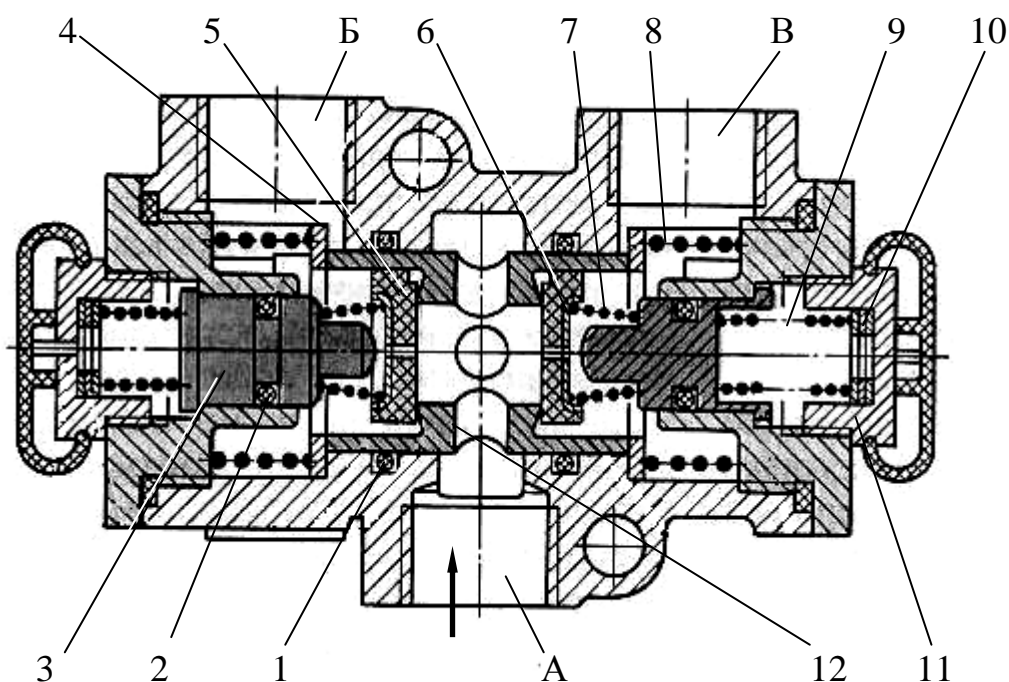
Двойной защитный клапан питающей части тормозного привода грузового автомобиля-тягача КАМАЗ-5320 (регулятор давления отключил компрессор от пневмосистемы): 1 и 2 – уплотнительные кольца; 3 – упорный поршень; 4 – упорное кольцо; 5 и 6 – клапаны; 7, 8 и 9 – пружины; 10 – регулировочные шайбы; 11 – пробка; 12 – центральный поршень; А – ввод от компрессора; Б – вывод в контур IV вспомогательной ТС; В – вывод в контур III стояночной и запасной ТС
